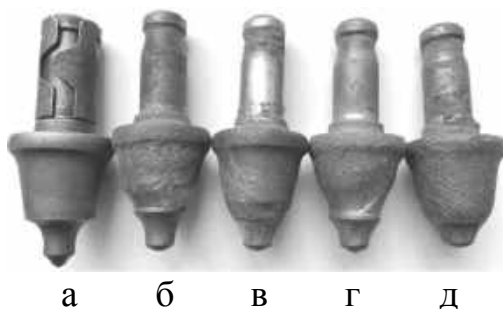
Різці барабанних фрез: а – новий; б-д – зношені
